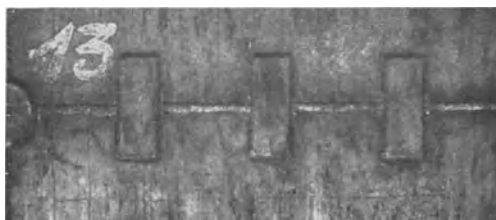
Mit Laschen gesicherte Schweißnaht.
